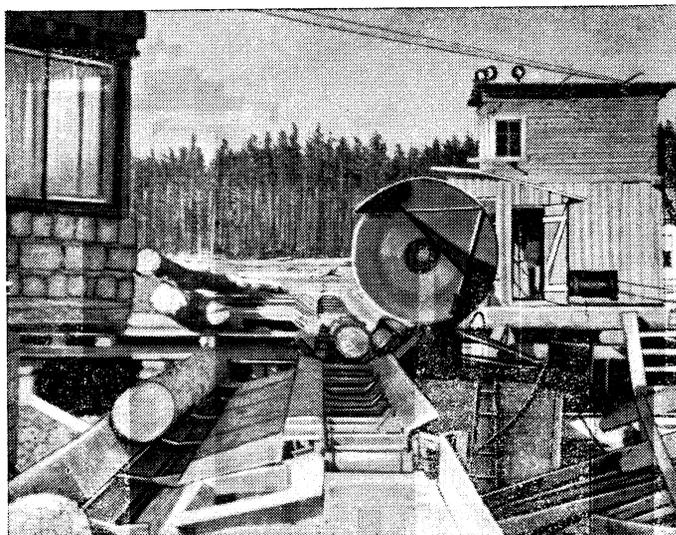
Общий вид полуавтоматической линии ПЛХ-3АС для раскряжевки хлыстов
